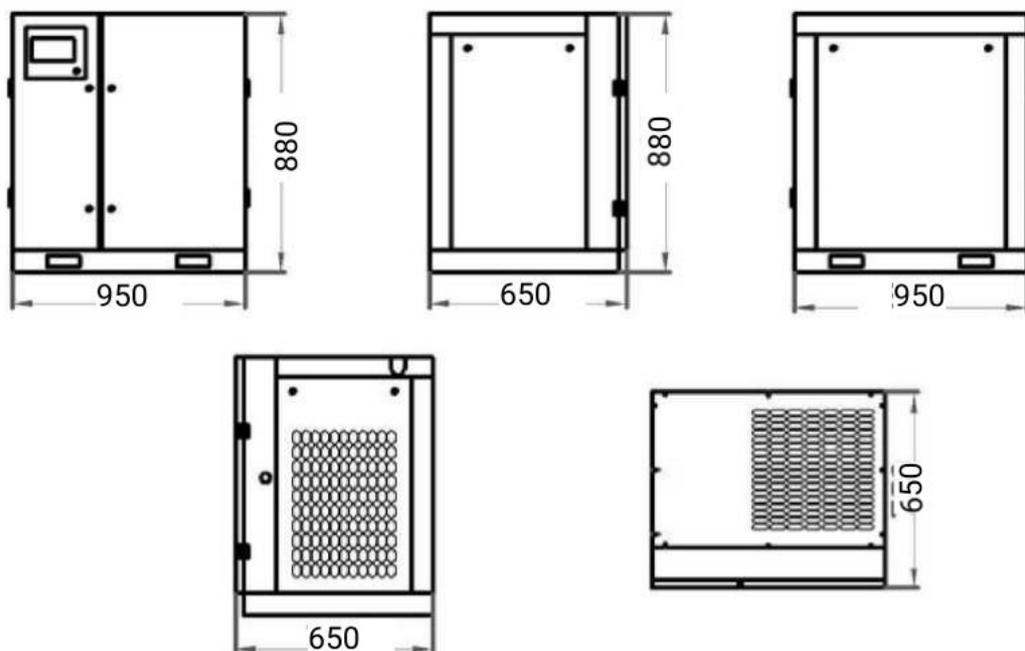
Габаритные размеры компрессоров BRM-7A
